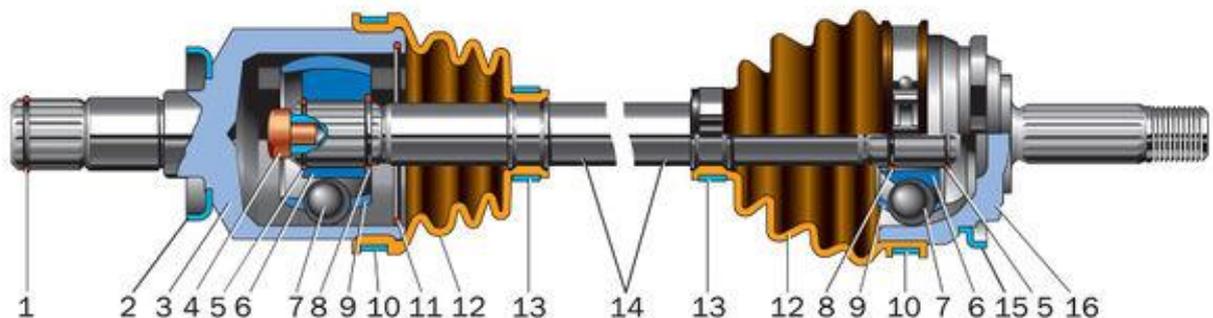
Универсальный шестишариковый карданный шарнир GKN:
